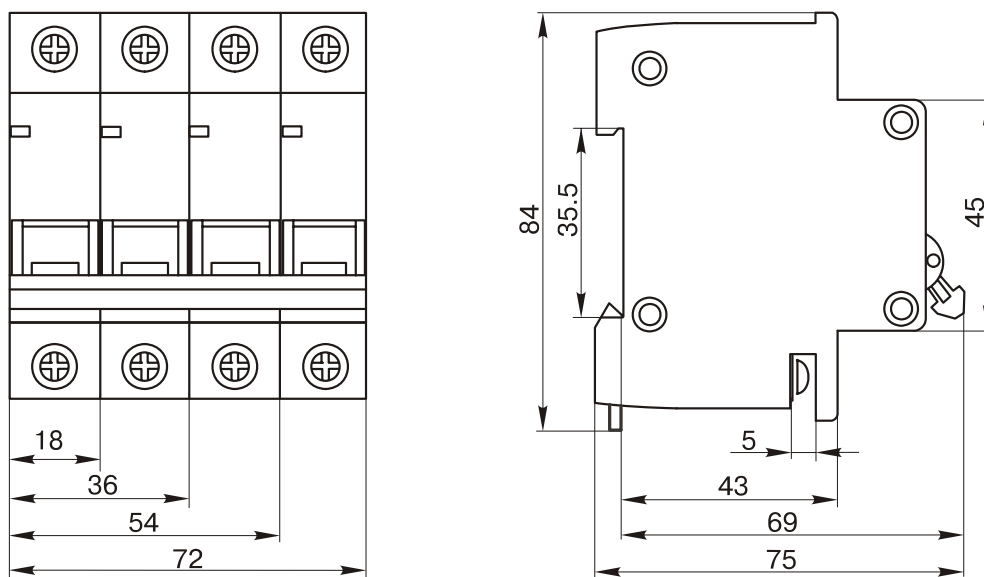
Габаритные и установочные размеры ВА47-29М
